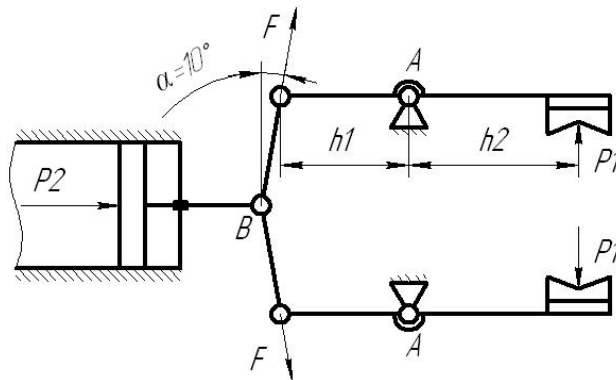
Розрахункова схема важільного механізму захвату
